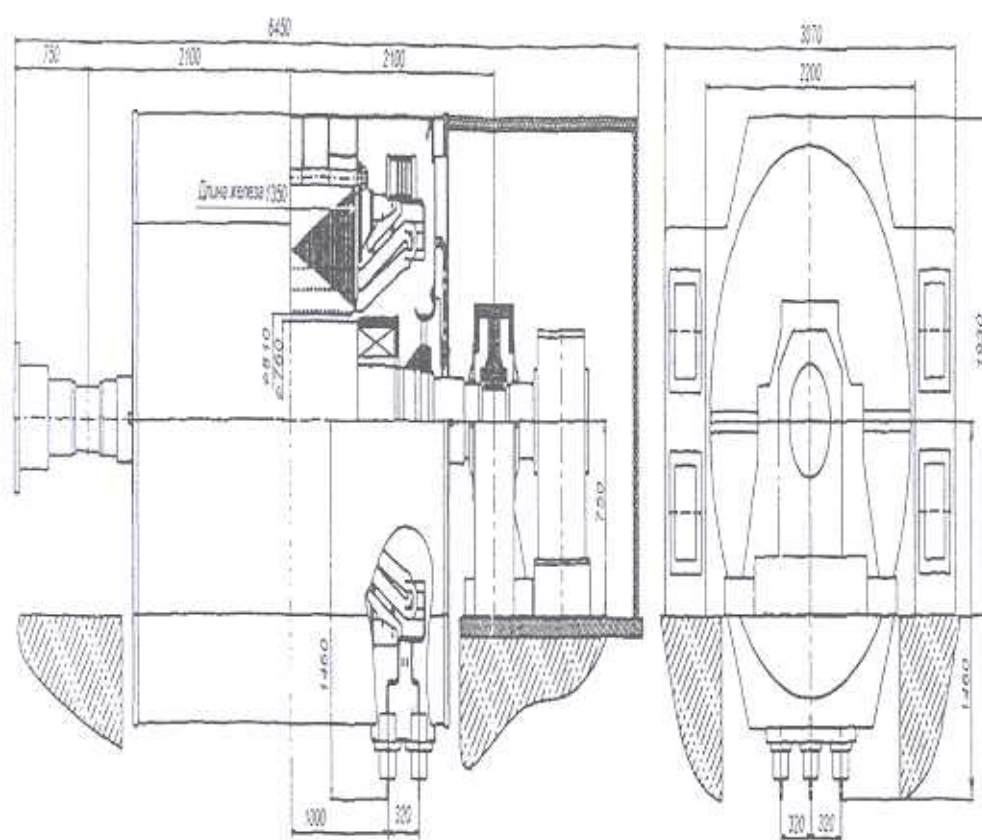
Установочный эскиз и габаритные размеры турбогенератора типа Т-16-2УЗ с бесщеточной системой возбуждения для сопряжения с паровой турбиной
